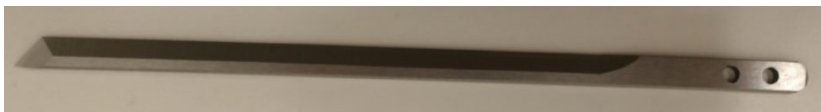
Нож CAD-06 для V-ATC2522-S11
